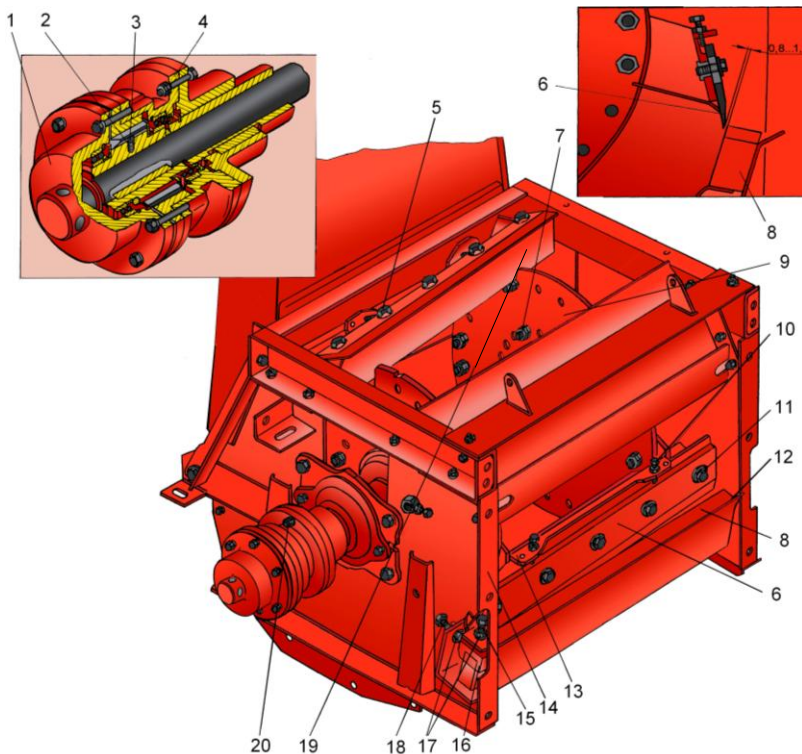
Измельчающий аппарат комбайна КСК-600: 1 – крышка обгонной муфты; 2 – пружина; 3 – шарик; 4 – корпус; 5 – болт крепления ножа; 6 – нож; 7 – болт крепления опоры ножа; 8 – противорежущий брус; 9 – диск; 10 – установочный винт; 11 – прижим ножа; 12 – чистик; 13 – опора ножа; 14 – рама; 15 – прижимной болт; 16 – прижим; 17 – контргайка; 18 – регулировочный болт; 19 – барабан; 20 – предохранительный болт
